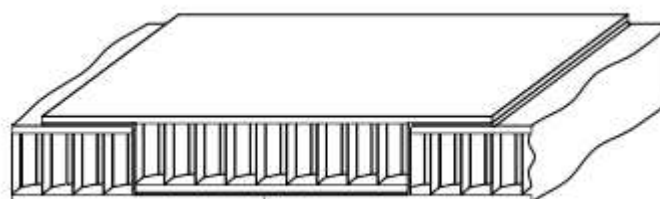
Spoj zpevněný přídavným materiálem [8]
